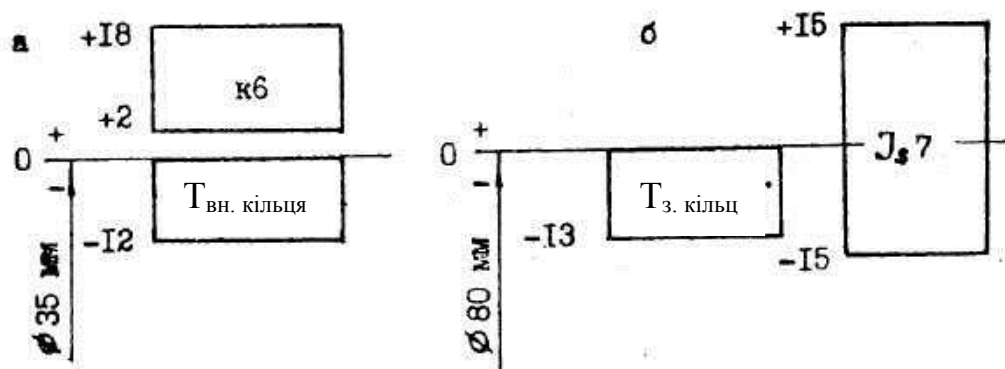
Схеми розташування полів допусків в з'єднаннях:
